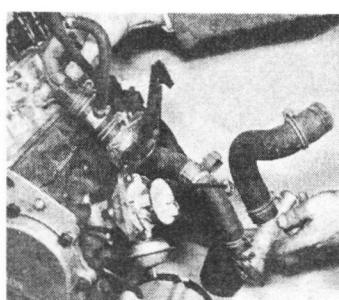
а. ... конструкцию патрубка впуска воды и шланга...
